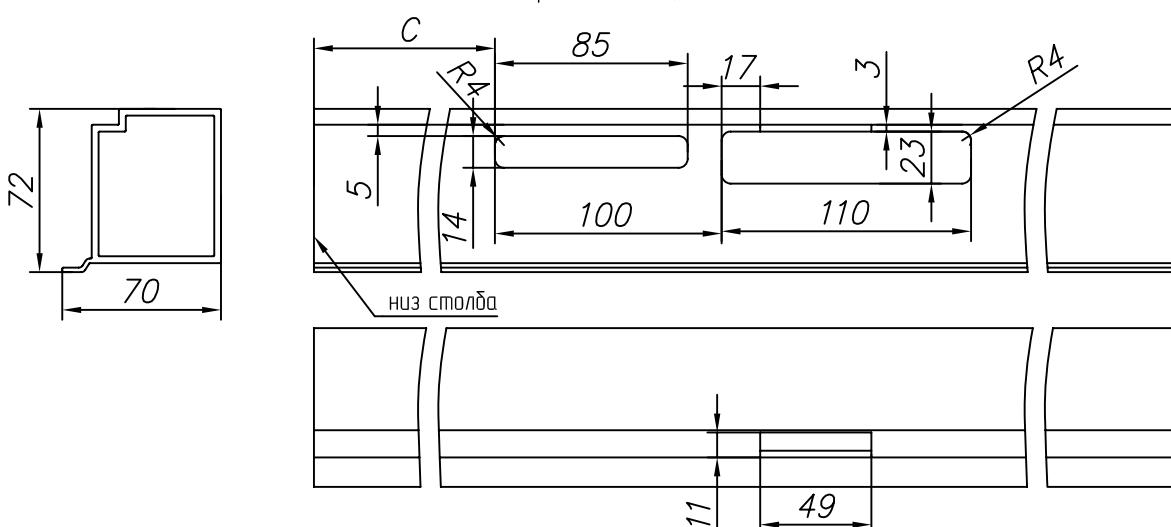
Изготовление столба притвора с пазом для автоматической защелки для калитки с правым открыванием (защелка R12HZ)
